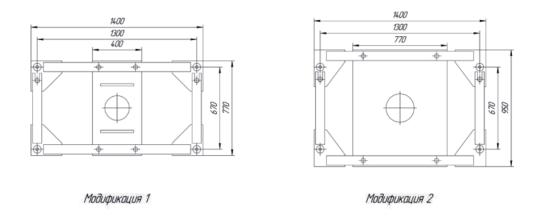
Габаритные и установочные размеры МАК-П (п)
